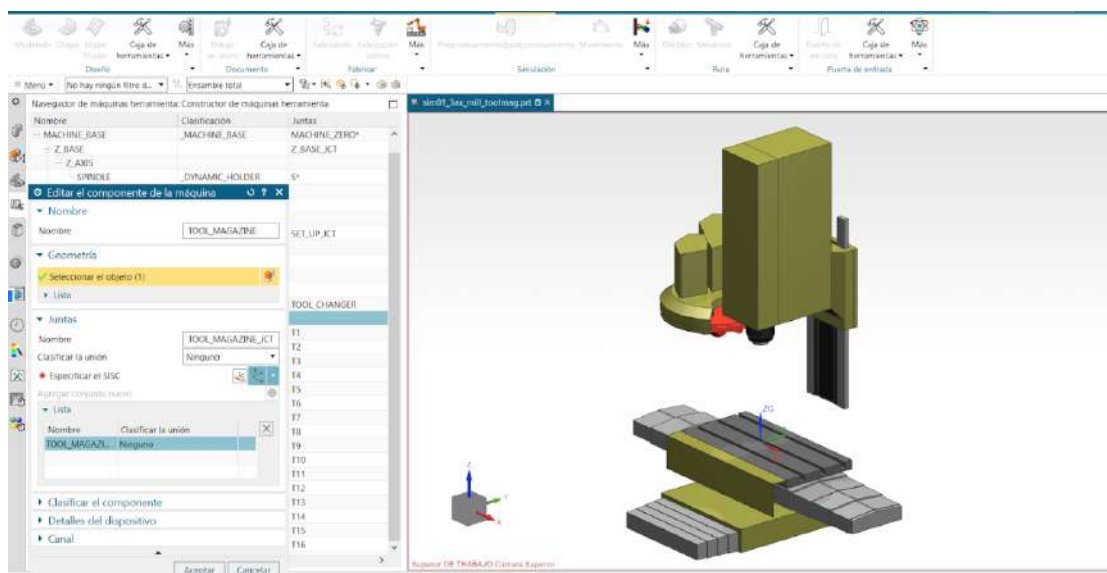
Definición del componente Cambiador Automático de Herramientas.
